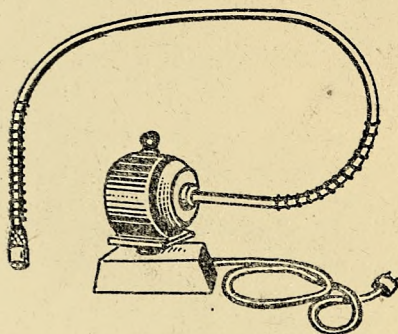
Шероховальный станок с гибким валом, укрепленный на верстаке
